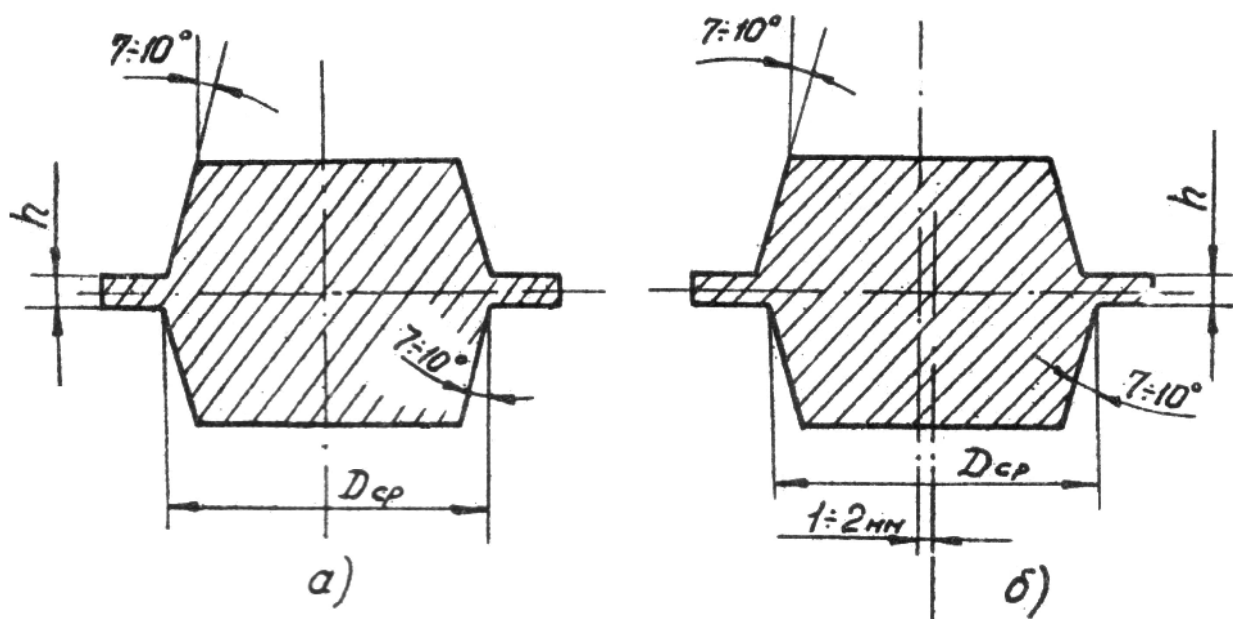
Эскизы штампованных поковок с заусенцем: а) качественная поковка; б) поковка с дефектом штамповки (смещение половинок штампа).
